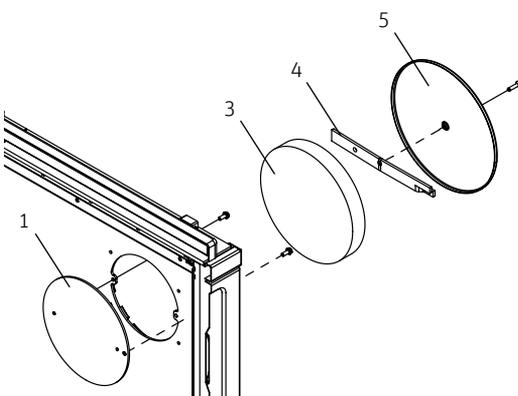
Montare la flangia cieca dietro, VestoWIN Premium 200/202
